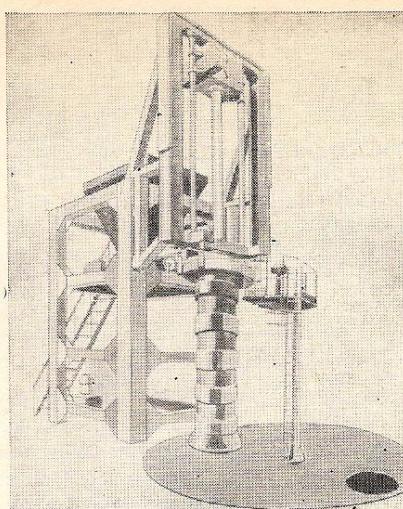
Станок СМЖ-329 для формования бетонных и железобетонных труб диаметром 800, 1000 и 1200 мм
